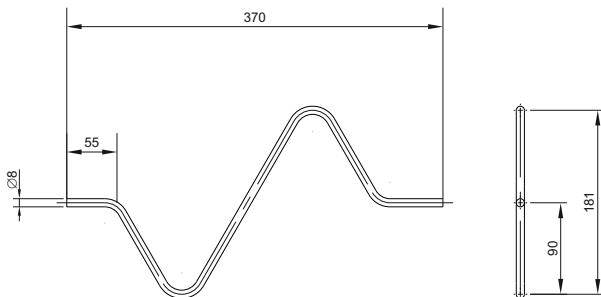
Габаритные размеры компенсатора / Figure 1 – Overall dimensions of the compensator /
